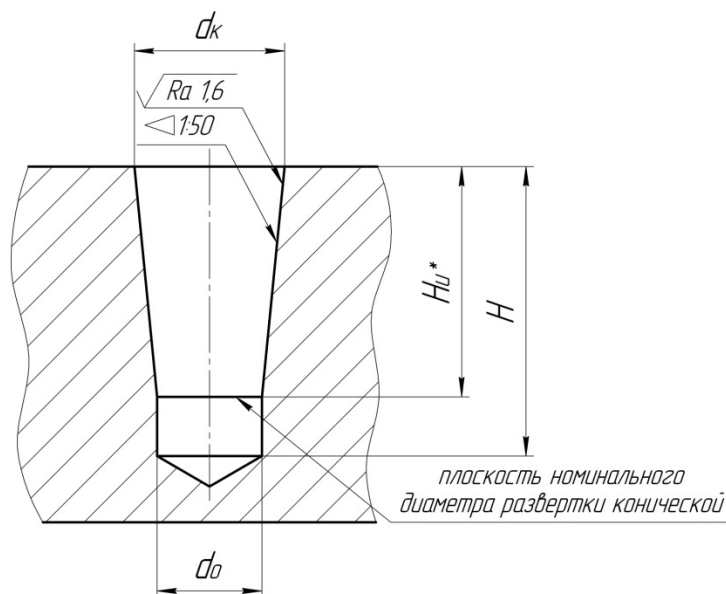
Место под установку штифта конического d_k – наружный диаметр отверстия под развертку коническую; d_o – диаметр отверстия под развертку коническую; H_n^* – размер справочный; H – глубина сверления отверстия под развертку коническую
